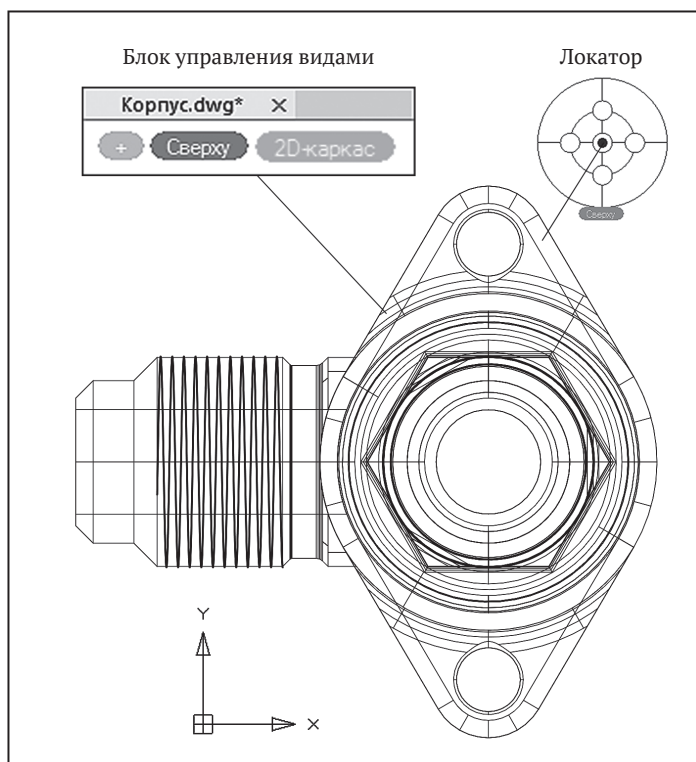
Способы № 1 и 2 образования Влада сверху 3D-модели детали «Корпус» (визуальный стиль Каркас)
